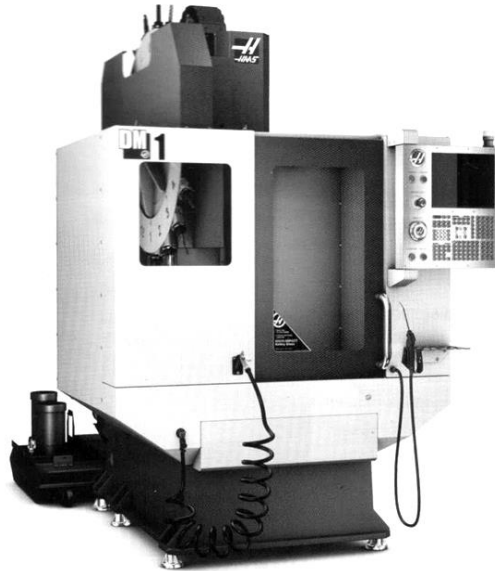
Загальний вигляд верстата з ЧПК свердлильно-різбонарізного центру DT-1
